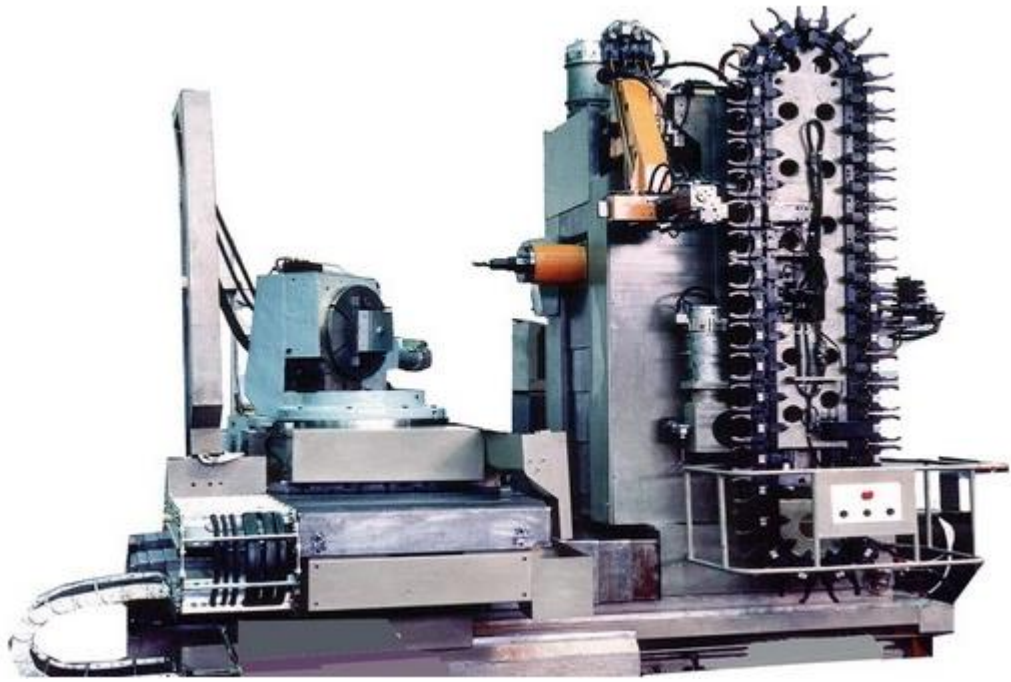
Горизонтальный обрабатывающий центр с цепным конвейером
